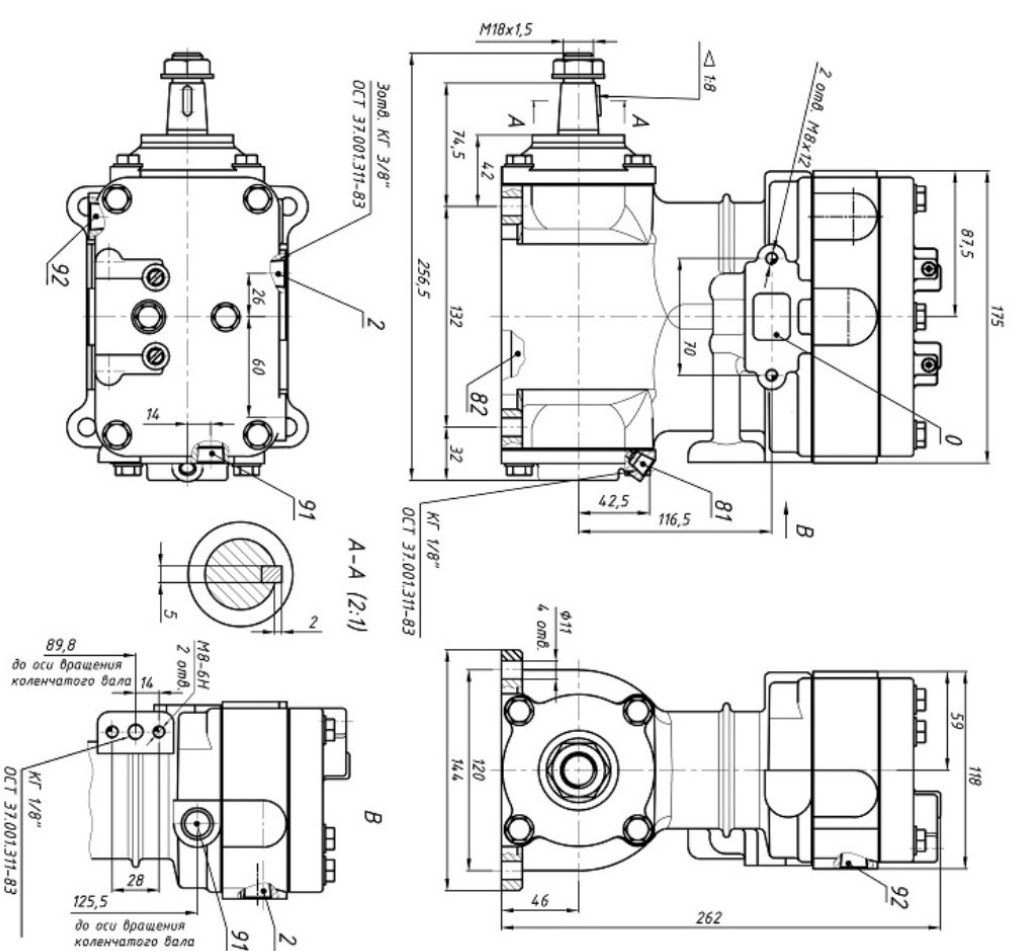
Присоединительные и установочные размеры компрессоров АМ.3509009-130.
